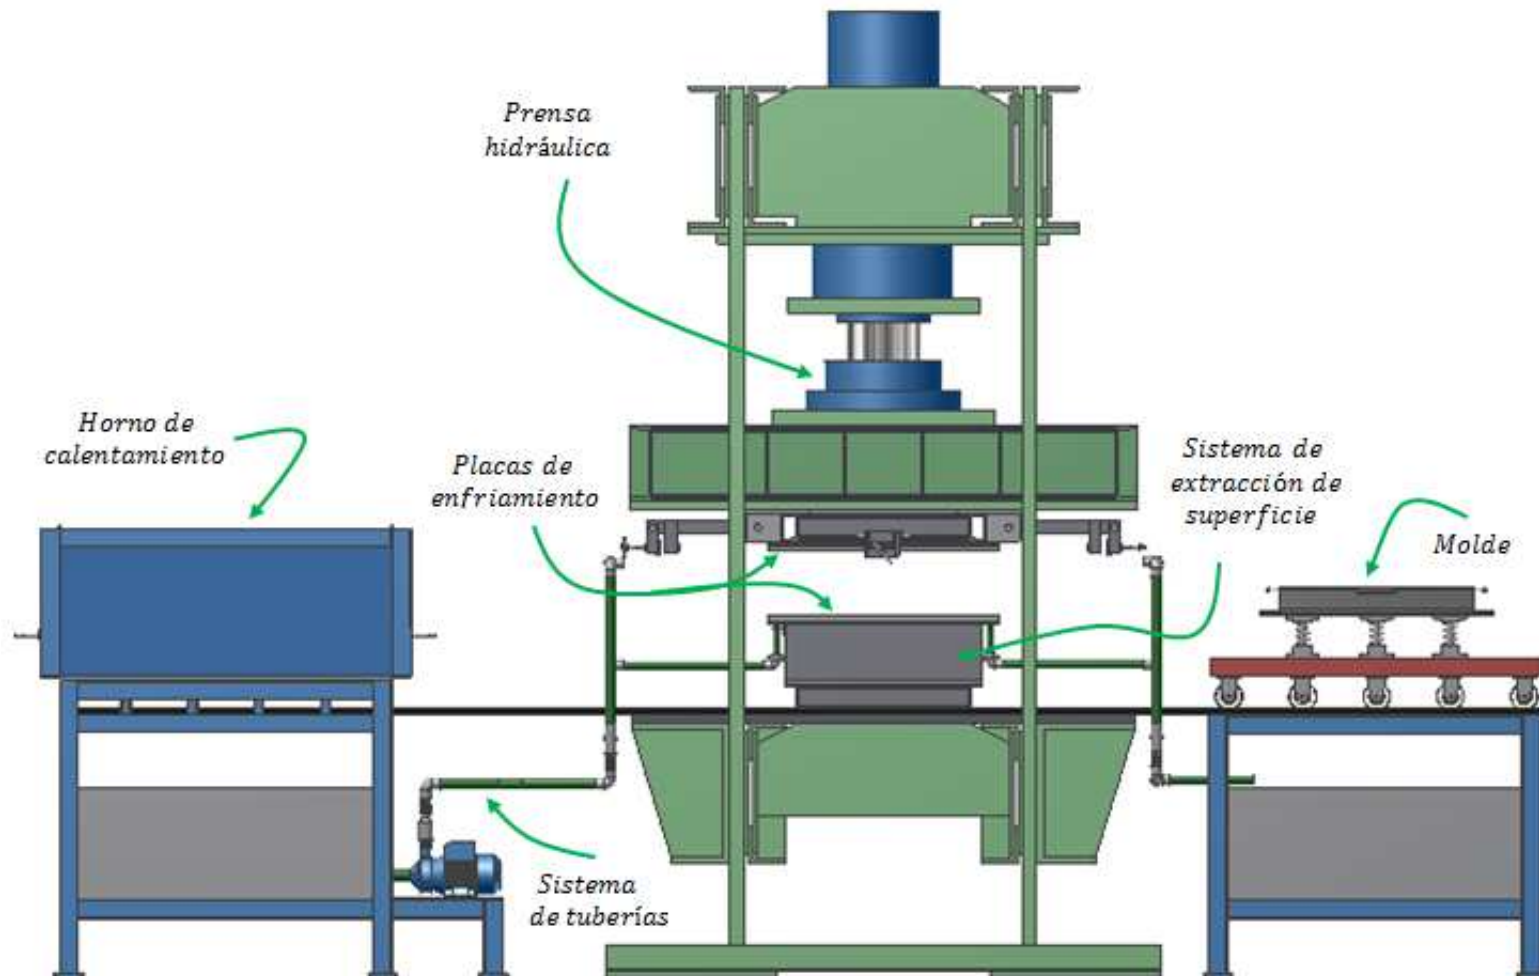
Vista frontal del modelo CAD del equipo de moldeo.
